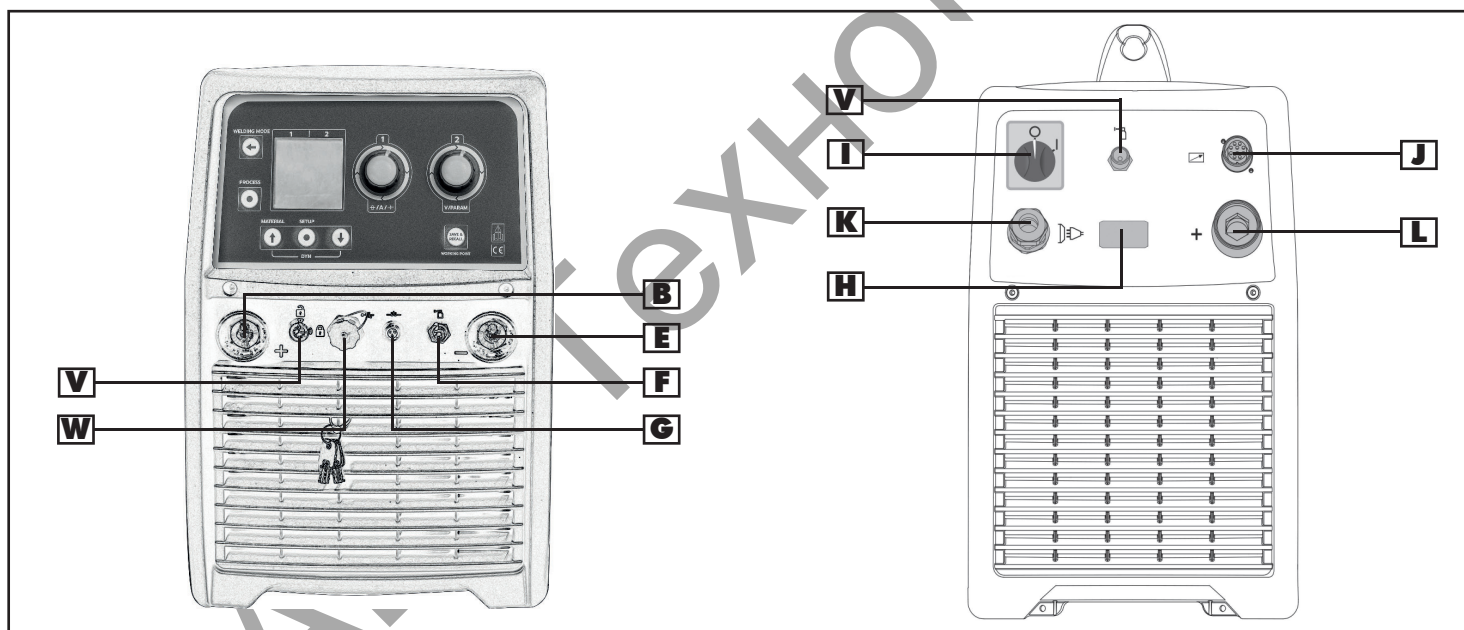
Вид передней и задней панелей сварочного инвертора с внешним устройством подачи проволоки
